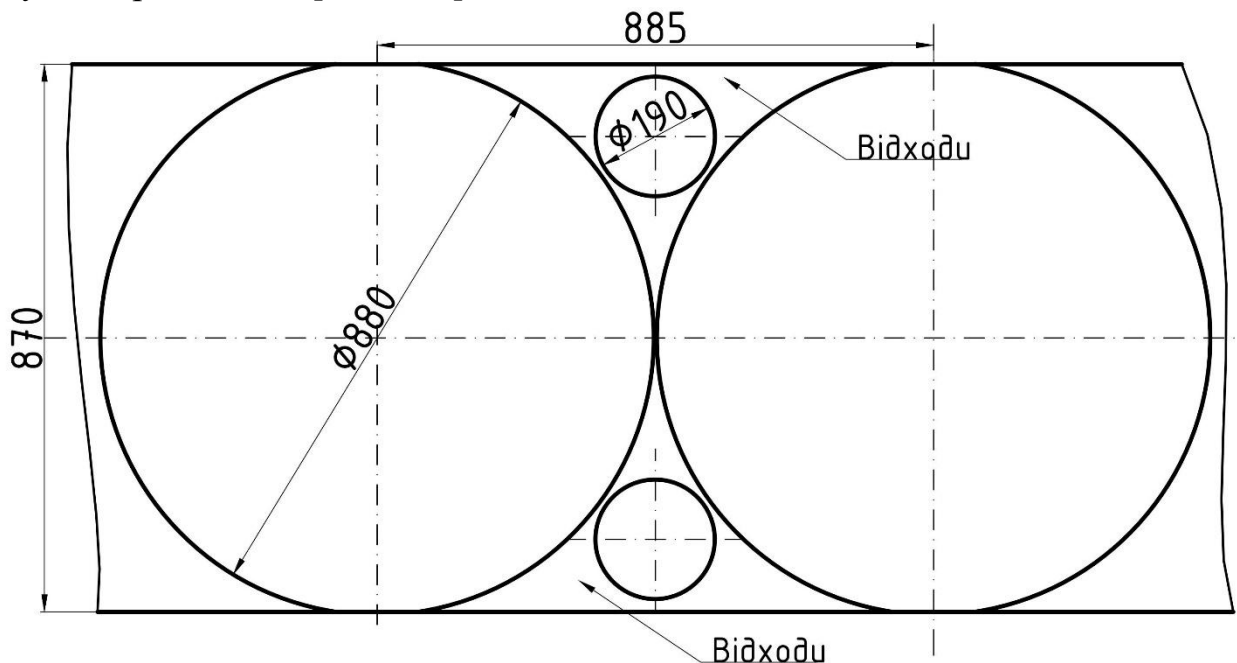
Схема розкрою заготовки $\varnothing 880$ мм по оптимальному варіанту
